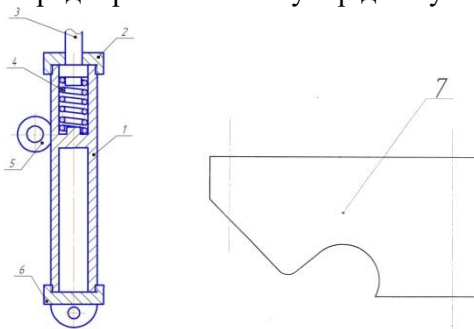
Предохранительный упор для кузова автомобиля – самосвала:
